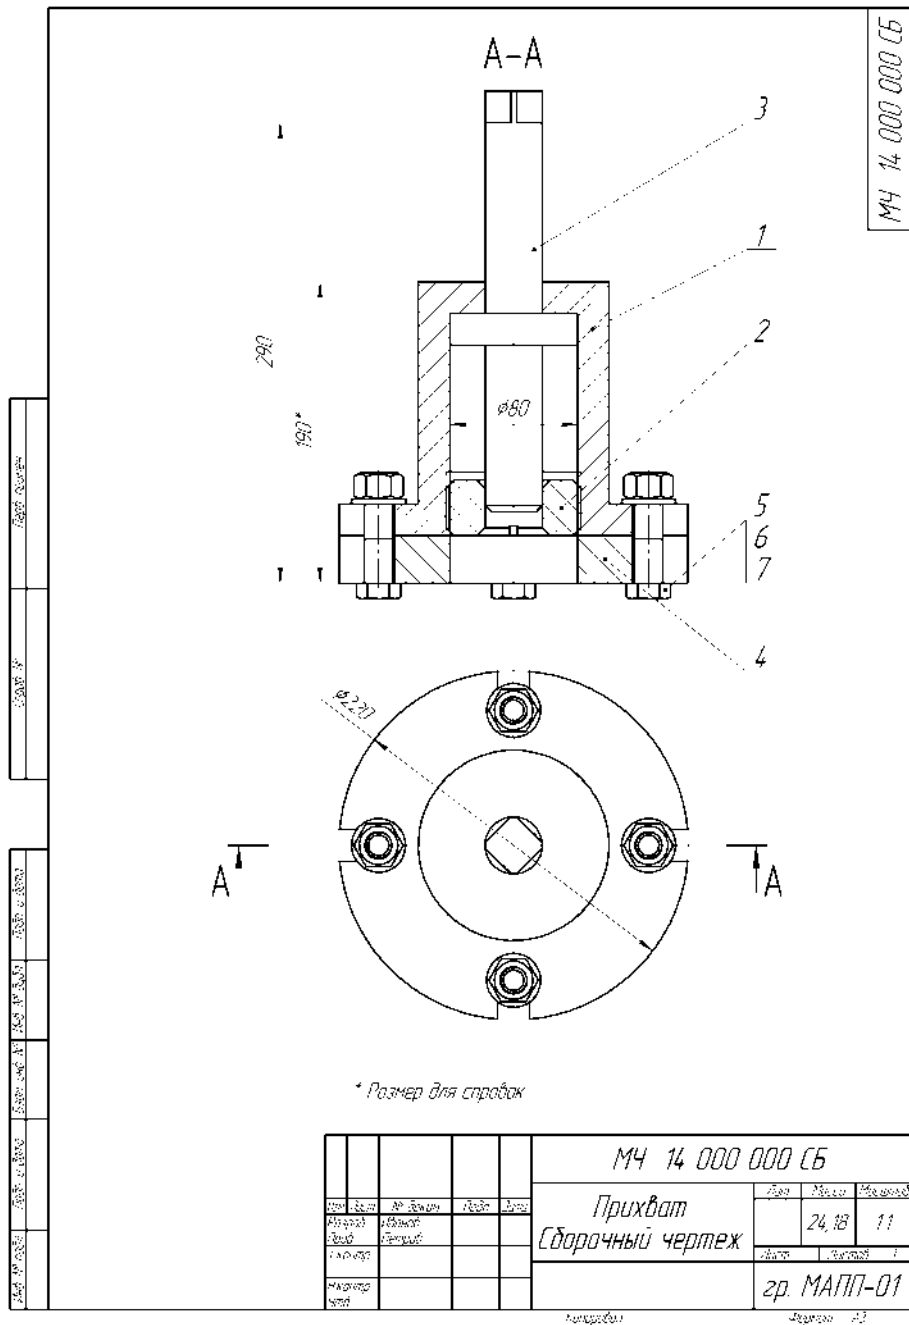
Размещение размеров и номеров позиций на чертеже
